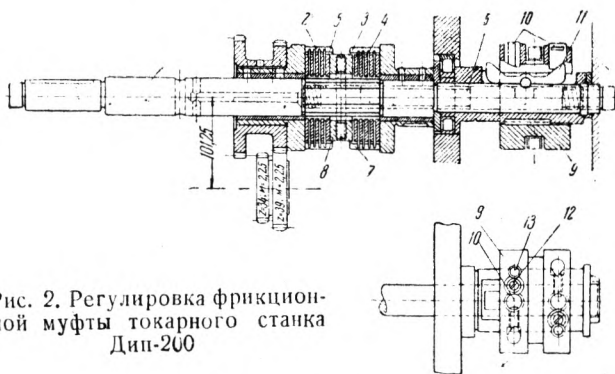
Регулировка фрикционной муфты токарного станка ДИП-200
